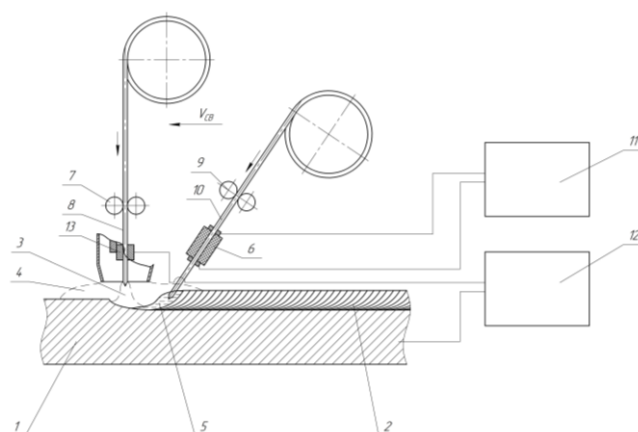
Схема процесса дуговой сварки с ДГП в защитном газе: 1 – основной металл, 2 – сварной шов, 3 – сварочная дуга, 4 – защитная атмосфера, 5 – сварочная ванна, 6 – подогревающий элемент, 7 – подающий механизм для сварочной проволоки, 8 – сварочная проволока, 9 – подающий механизм для ДГП, 10 – дополнительная горячая присадочная проволока, 11 – источник питания для ДГП, 12 – основной источник питания, 13 – контактный наконечник
